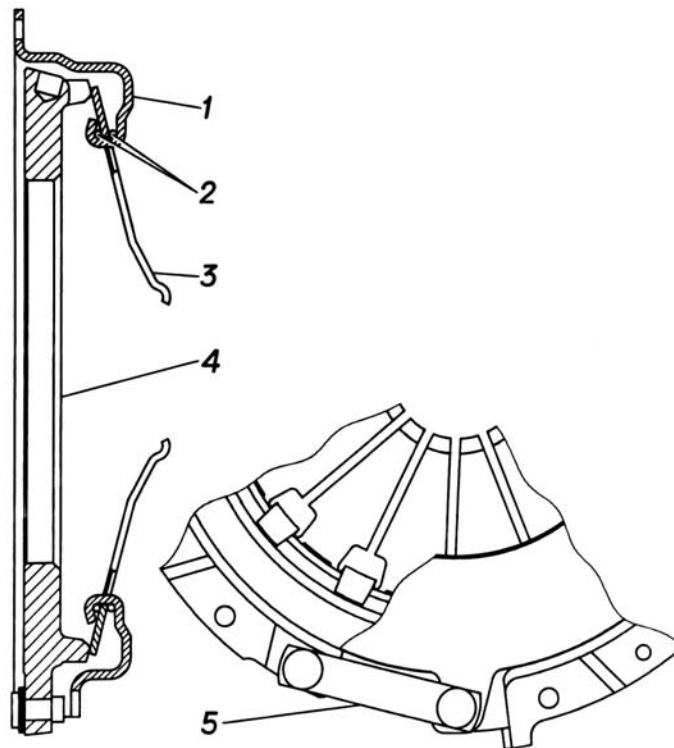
Ведущий диск сцепления в сборе: 1 - кожух; 2 - опорные кольца; 3 - нажимная диафрагменная пружина; 4 - нажимной диск; 5 - соединительная пластина
